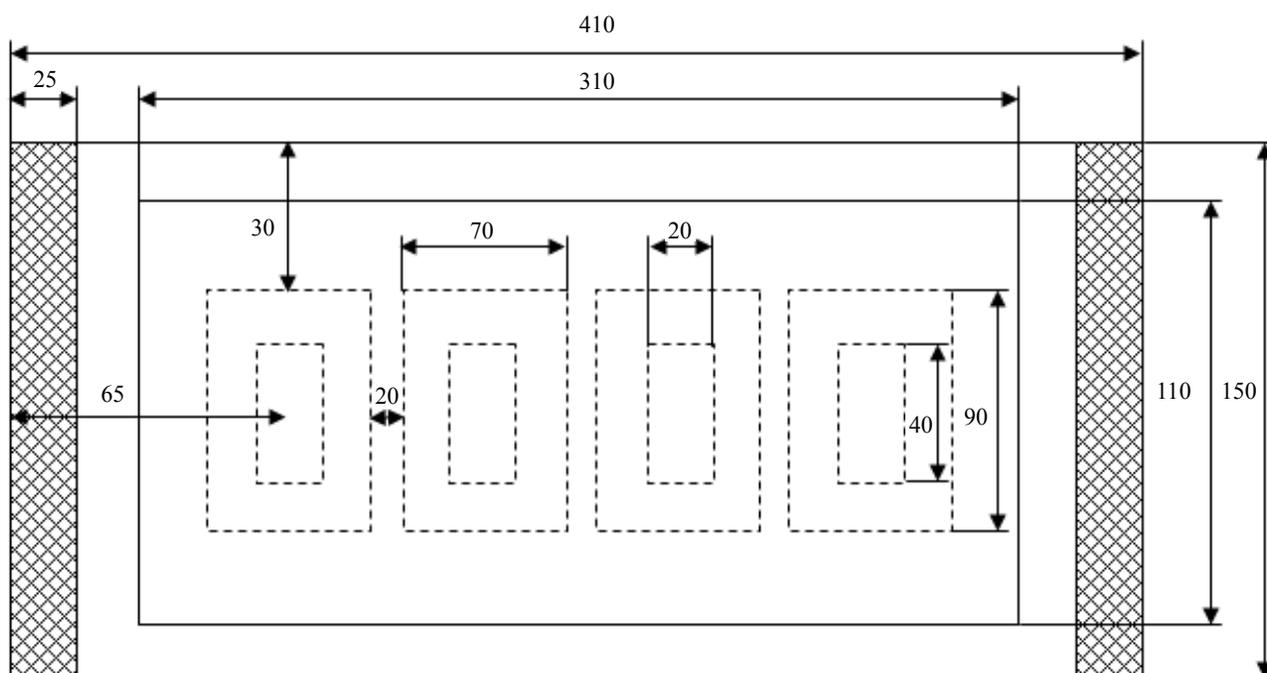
Эскизный рисунок опытного образца ТЭС с основными геометрическими размерами
